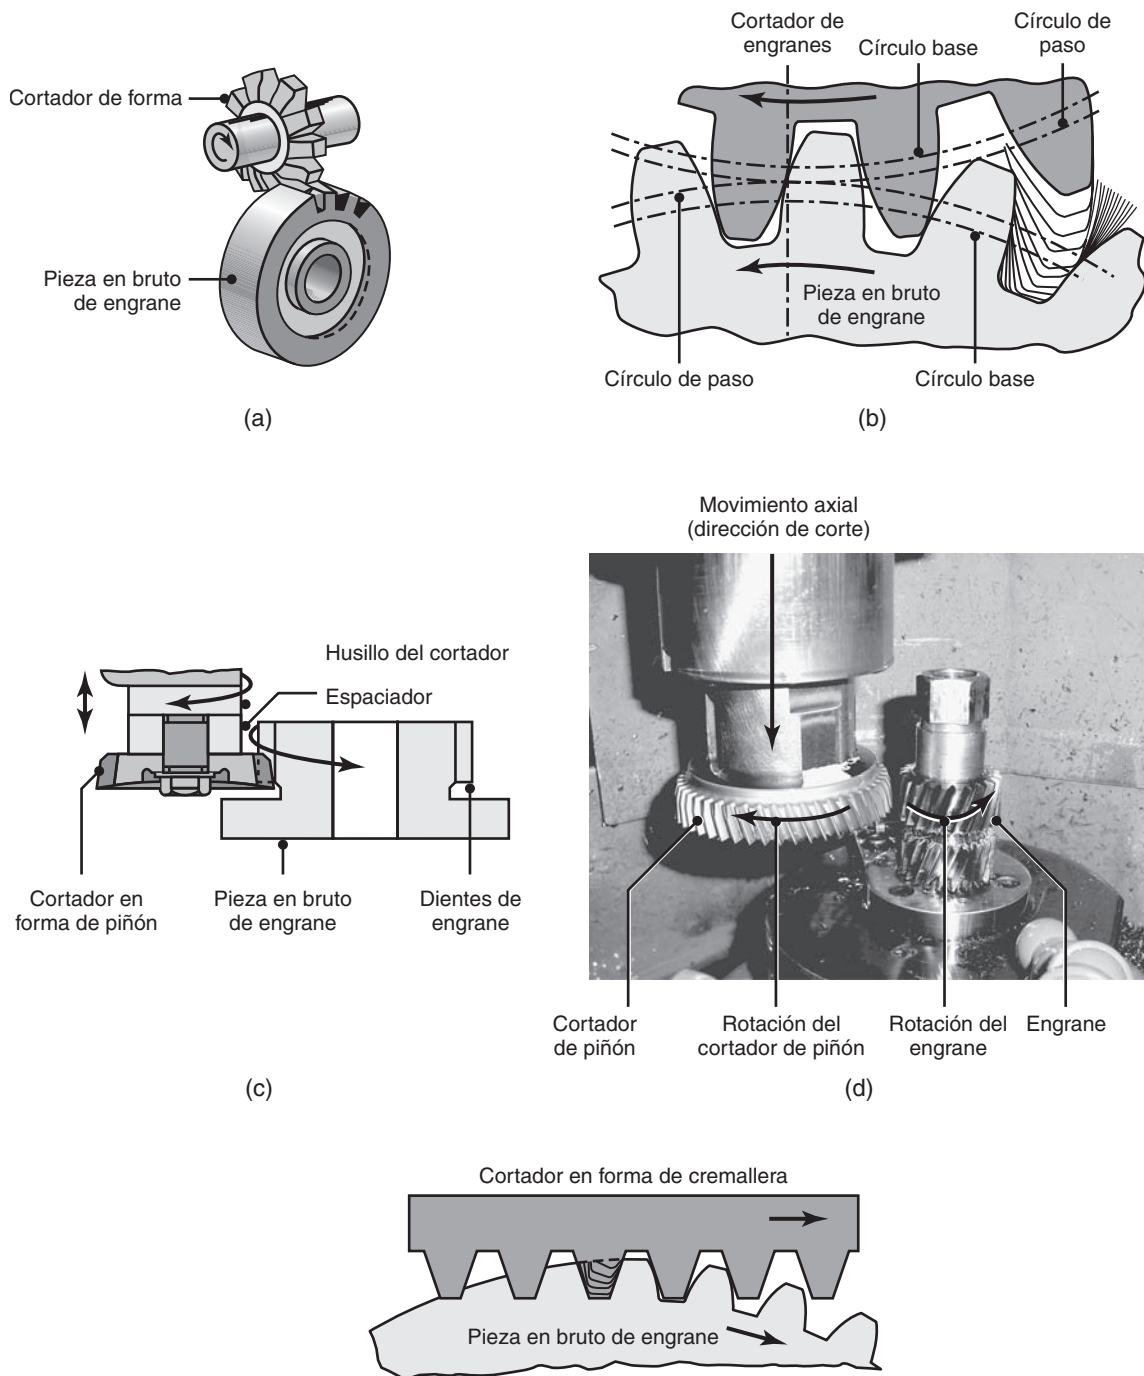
(a) Producción de dientes de engrane en una pieza en bruto por corte de forma. (b) Esquema de engrane que se genera con un cortador de engranes en forma de piñón. (c) y (d) Engrane que se genera en una cepilladora de engranes utilizando un cortador en forma de piñón. Obsérvese que el cortador se mueve alternativamente en la dirección vertical. (e) Engrane que se genera con cortador en forma de cremallera. *Fuente:* (d) Cortesía de Schafer Gear Works, Inc.
